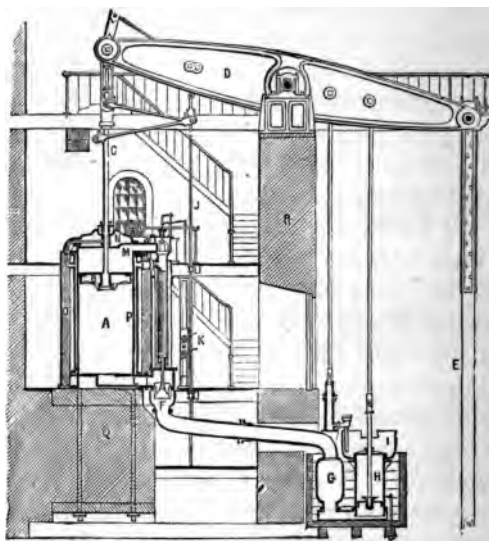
Machine à épuisement de Cornouailles. 1878. — Coupe.
